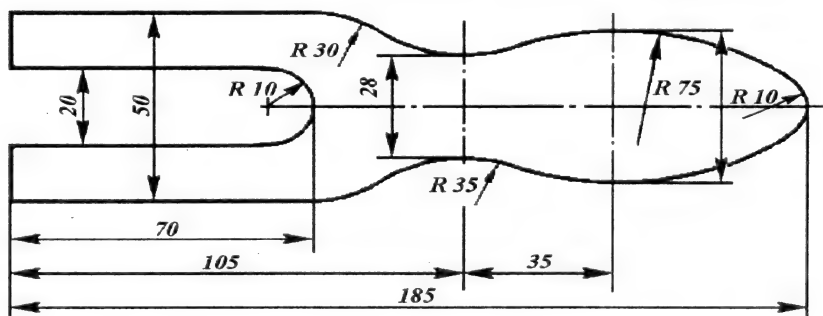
Упоры для поршней для облегчения надевания блока цилиндров
